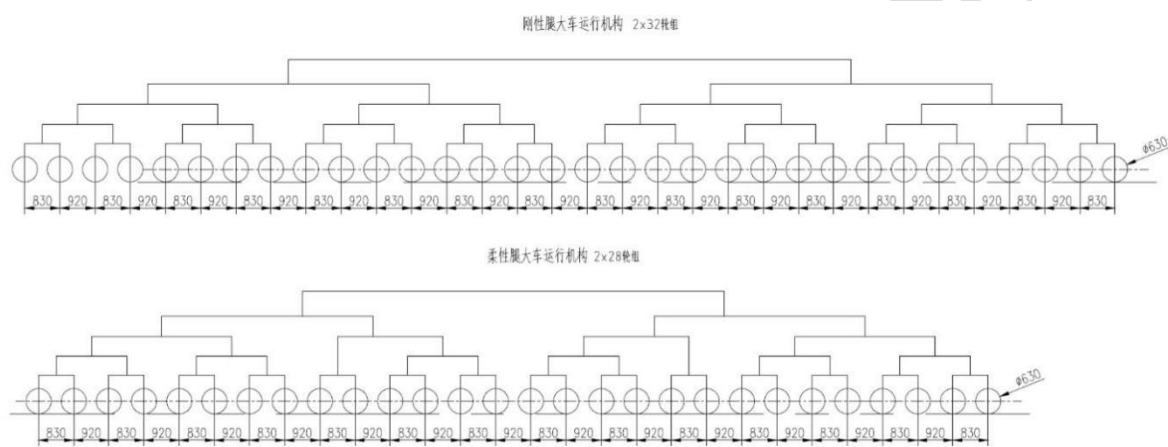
龙门吊轨道支腿轮距布置断面图
